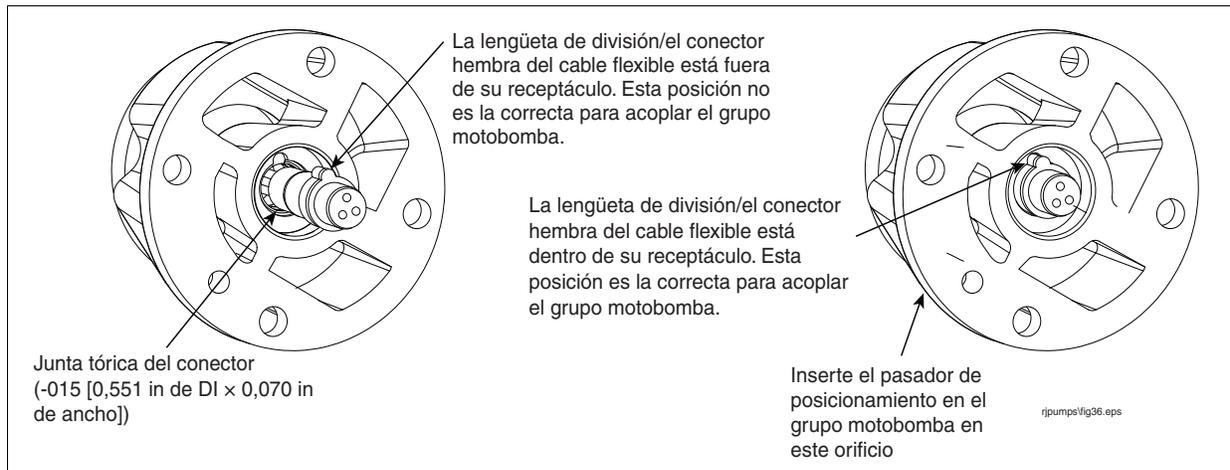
Compruebe que el conector hembra del cable flexible esté bien colocado
